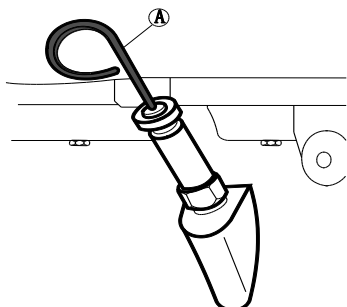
Inspección de nivel de cárter de aceite de motor diesel
